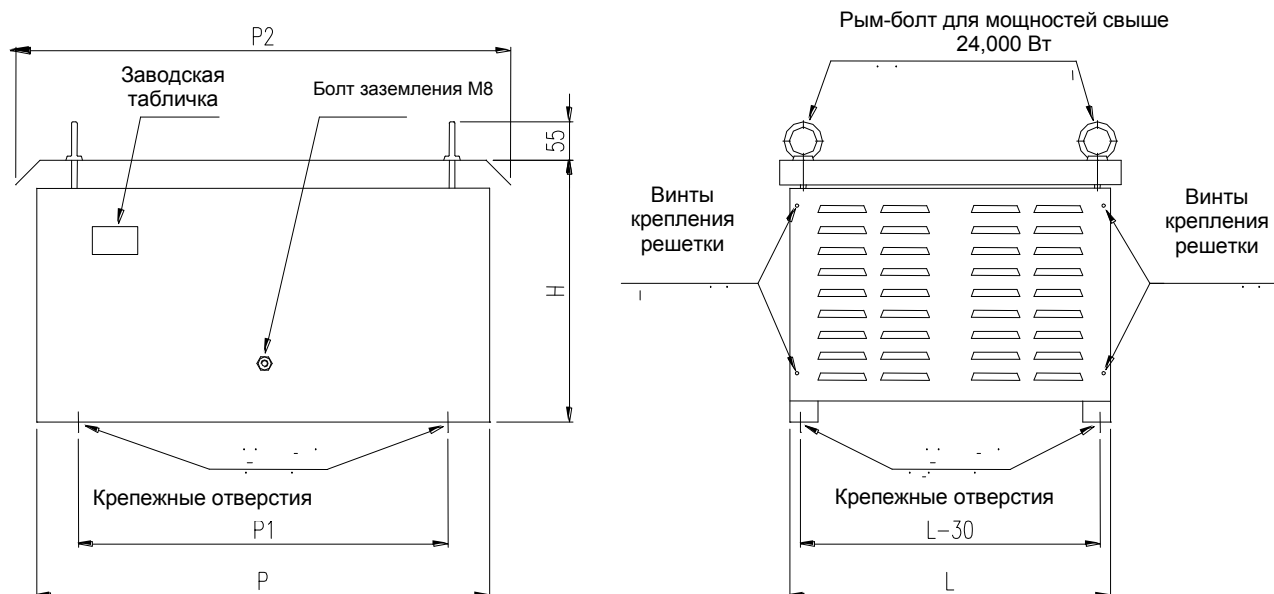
Габаритные и установочные размеры корпусного резистора IP23
